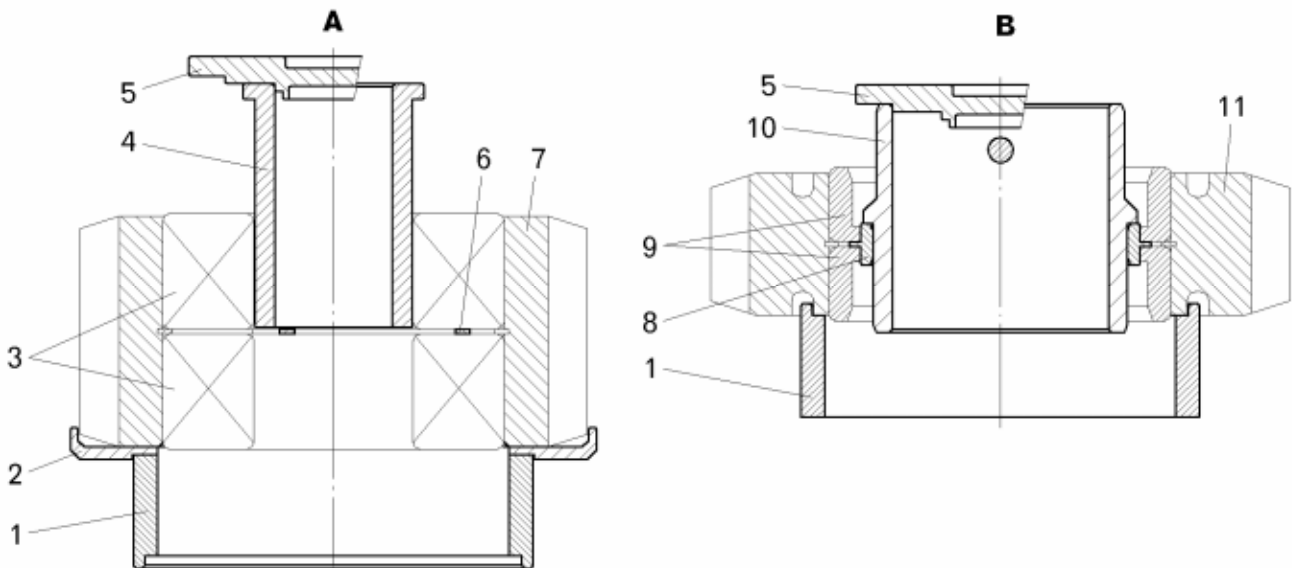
Приспособление для демонтажа подшипников из сателлитов:
